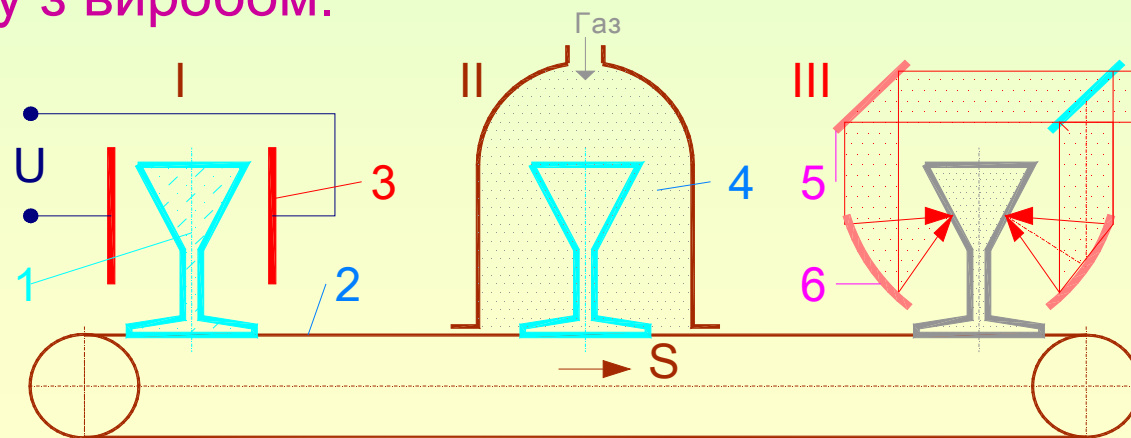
Схема засобу нанесення газової сажі на поверхню заготовки
